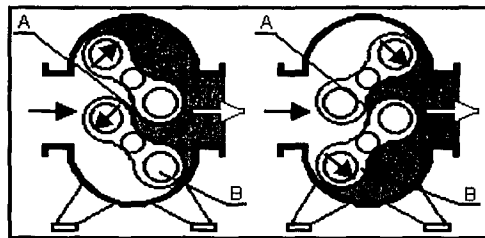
Compresor Root. A) Juego entre rotores. B) Rotor motriz.
